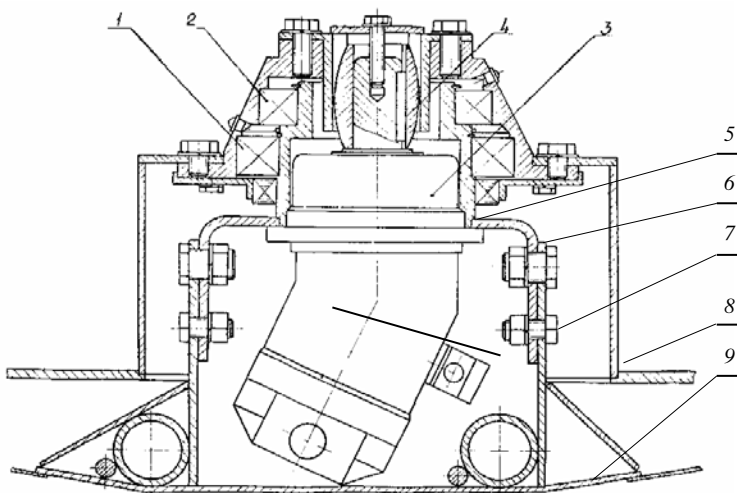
Привод двухроторного рабочего органа: 1 – подшипники внутренние; 2 – подшипники наружные; 3 – гидромотор; 4 – шлицевая втулка; 5 – уплотнение; 6 – стакан; 7 – болты; 8 – колпак; 9 – опора [11]
